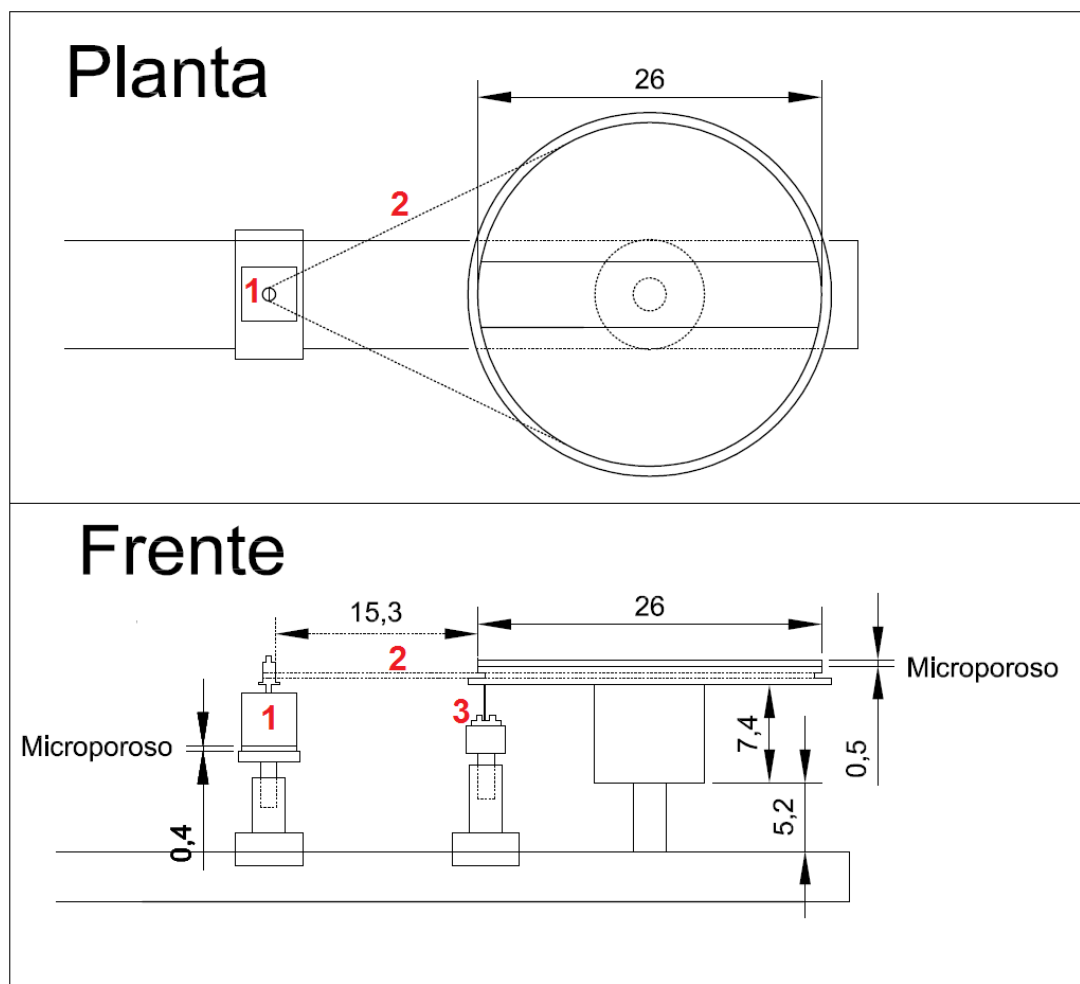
Esquema de la parte mecánica ligada al motor M2. (1) Motor M2,(2) faja dentada y (3) sensores infrarrojos. Las medidas están en cm.
